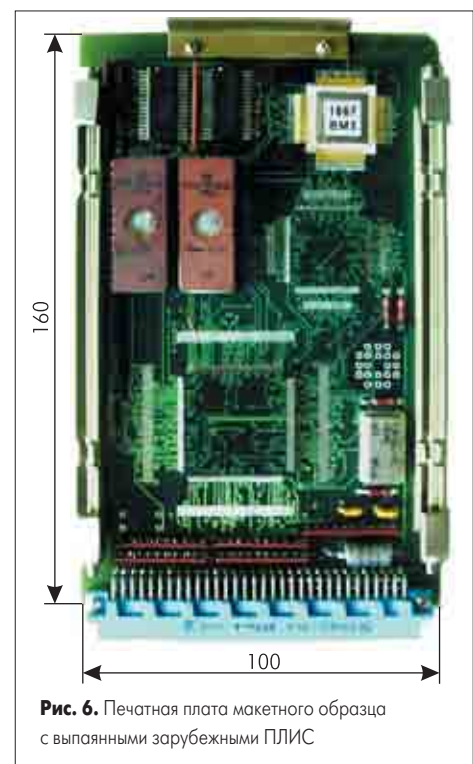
Печатная плата макетного образца с выпаянными зарубежными ПЛИС
